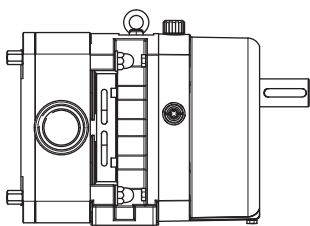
Máquina incompleta: bomba sin motor, acoplamiento y bastidor base, ejemplo basado en la FL 100
